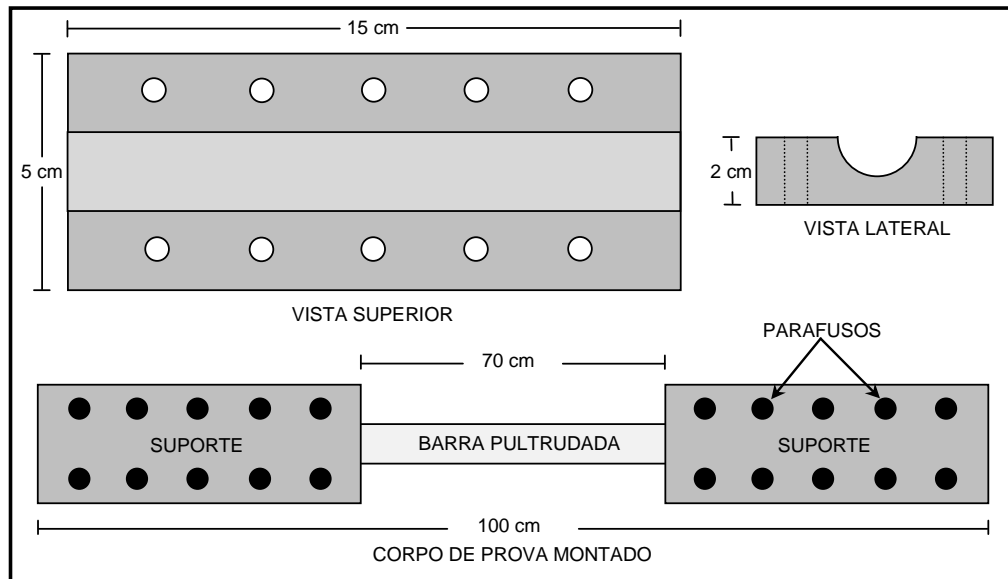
Dimensões dos suportes especiais de alumínio e montagem dos corpos de prova.
